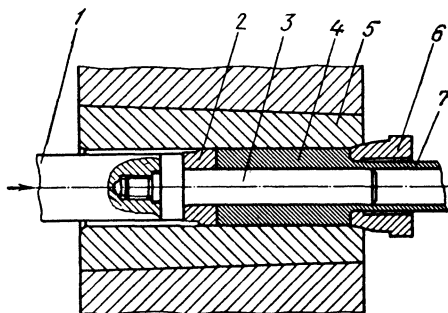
Схема прессования полого профиля из полой заготовки:
